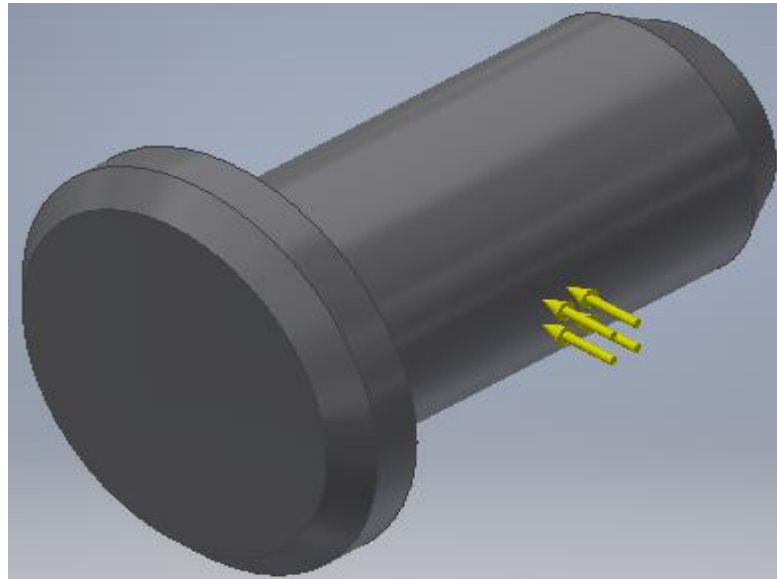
Fuerza distribuida que actúa sobre el pin de unión. Fuente: Elaboración propia.
